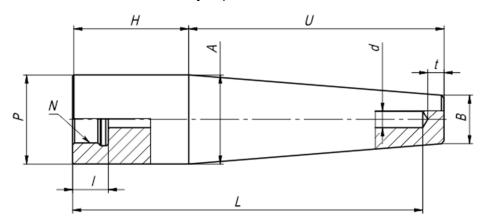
Гильза под приварку в стенку трубопровода (Weld-in), цельноточёная, коническая, под неподвижный штуцер.
